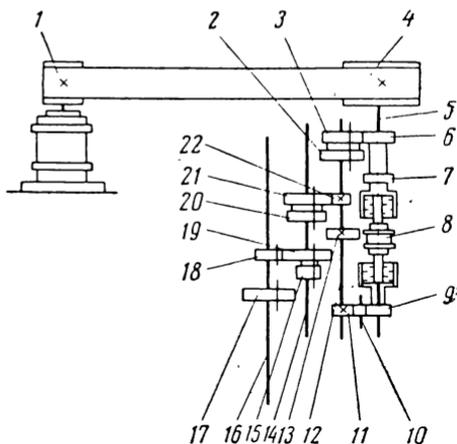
Схема коробки скоростей с подвижными блочными зубчатыми колесами и реверсивной дисковой фрикционной муфтой
